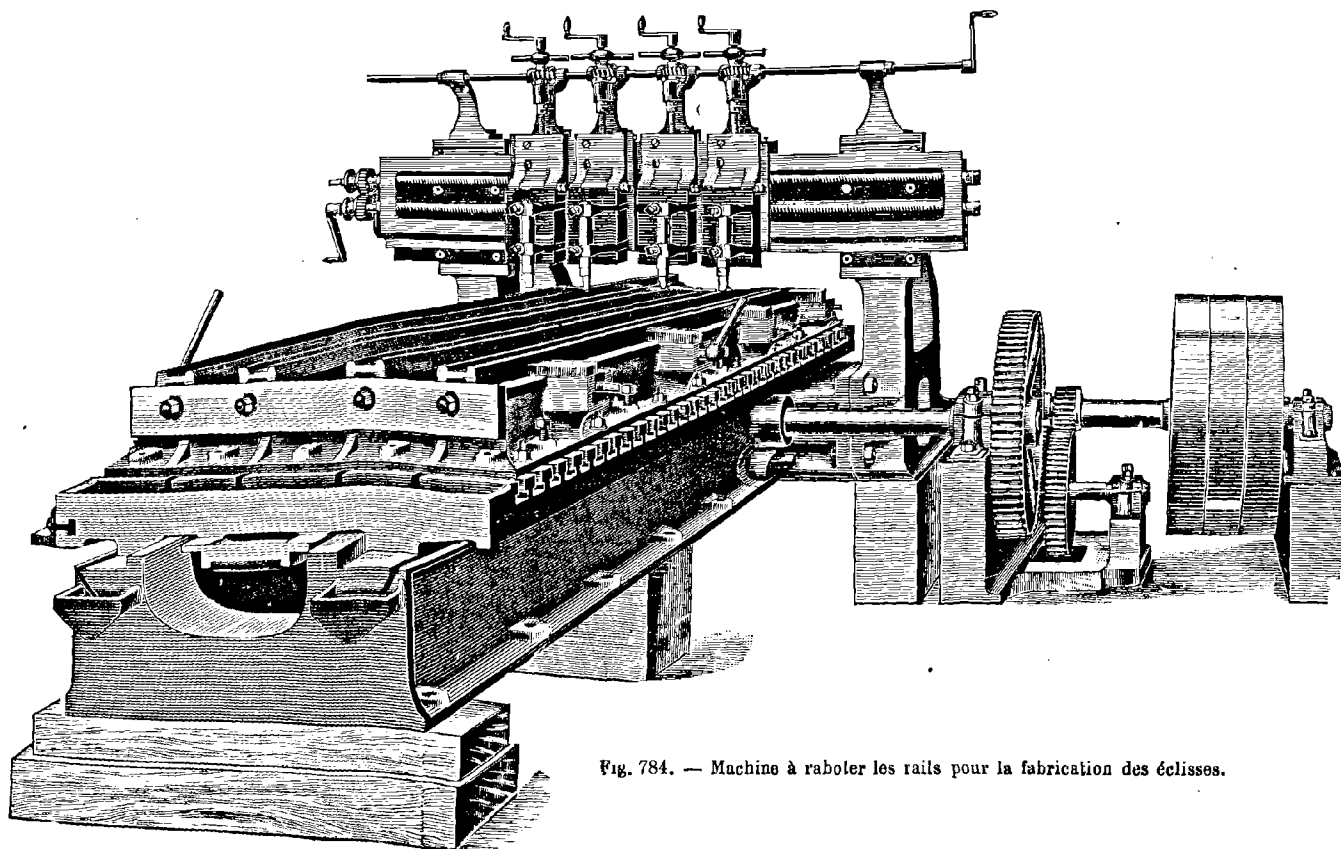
Machine à raboter les rails pour la fabrication des éclisses.
